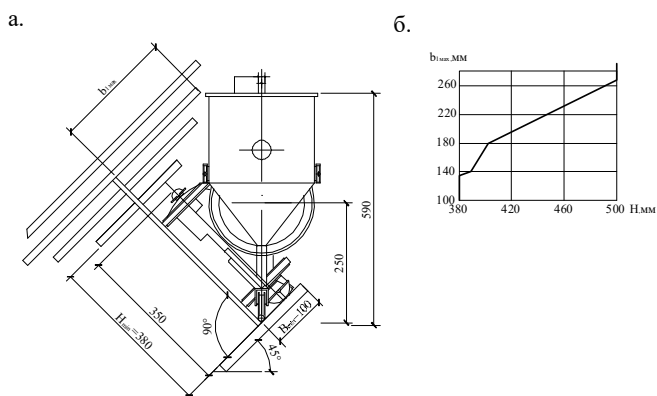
Доступность наложения швов при автоматической сварке балок в положении “в лодочку”. а) установка сварочного автомата, б) предельные размеры свариваемого двутавра
